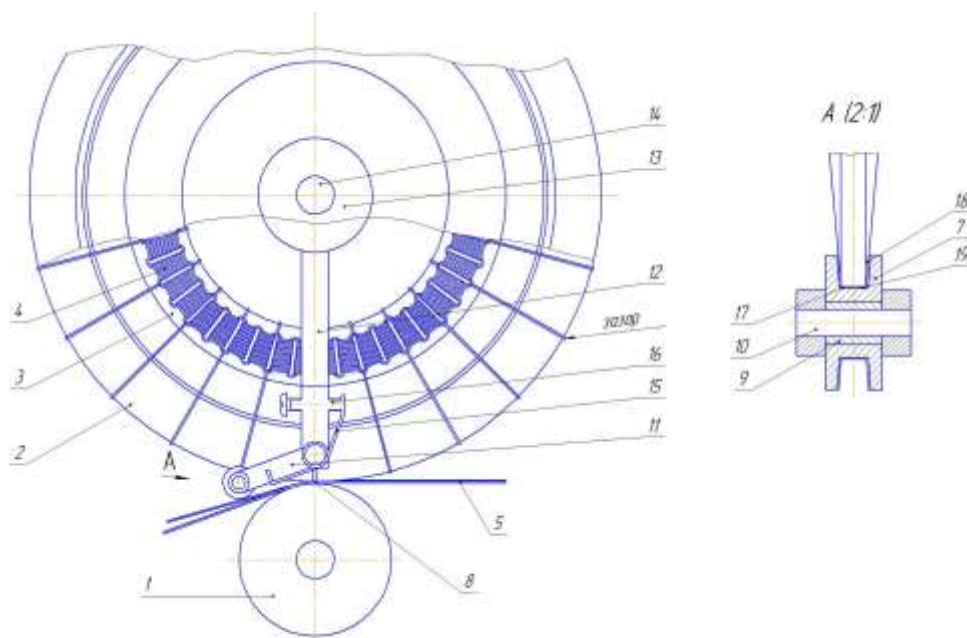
Ультразвуковая сварочная головка
